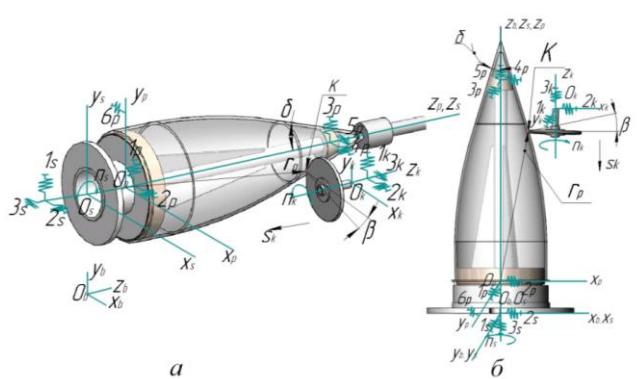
Схеми шліфування при використанні: а – токарного верстата, оснащеного агрегатною шліфувальною головкою та системою прямого копіювання (Варіант I); б – технологічного обладнання з механізмами паралельної кінематики, вбудованим обертовим столом і з системою ЧПК (Варіант II)
